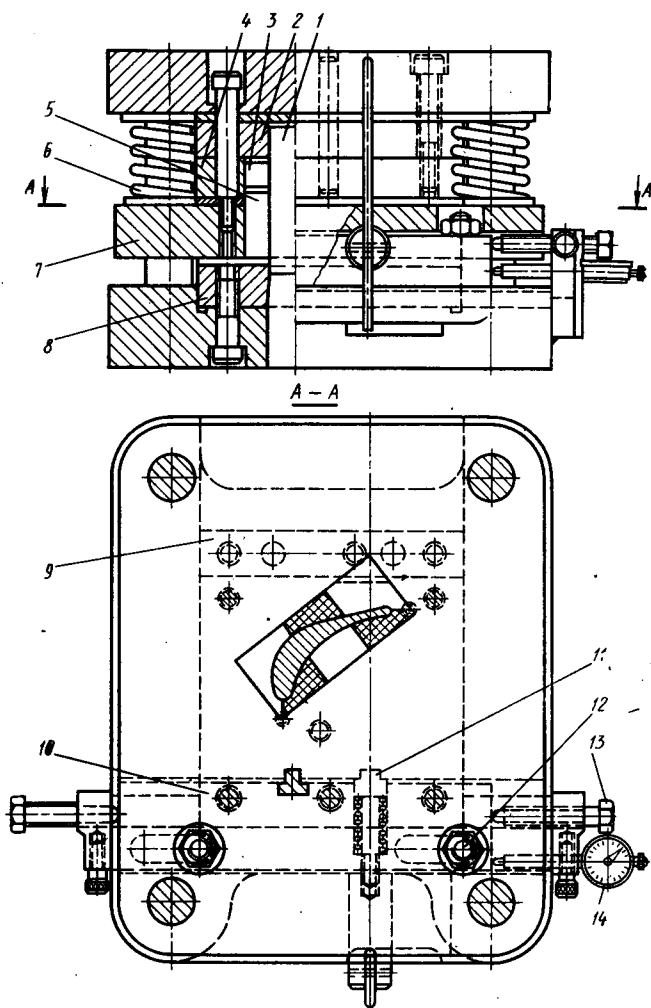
Штамп для пробивки фасонных отверстий в бандажах сварных диафрагм
